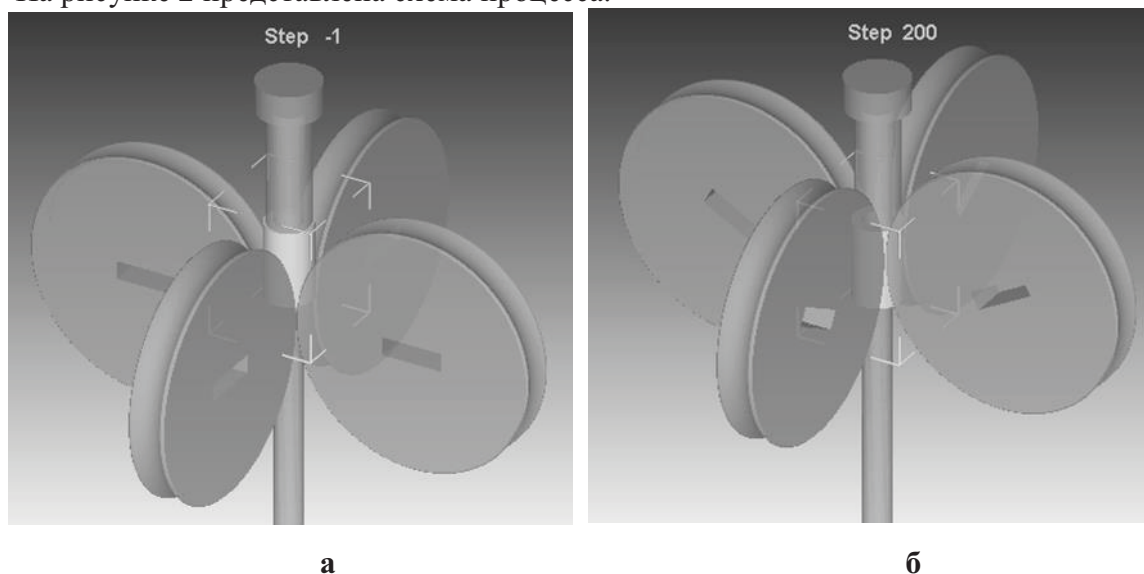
Схема обжатия трубной заготовки волочением (прокаткой) в неприводных роликах (валках): а - начальное положение; б - установившаяся стадия
